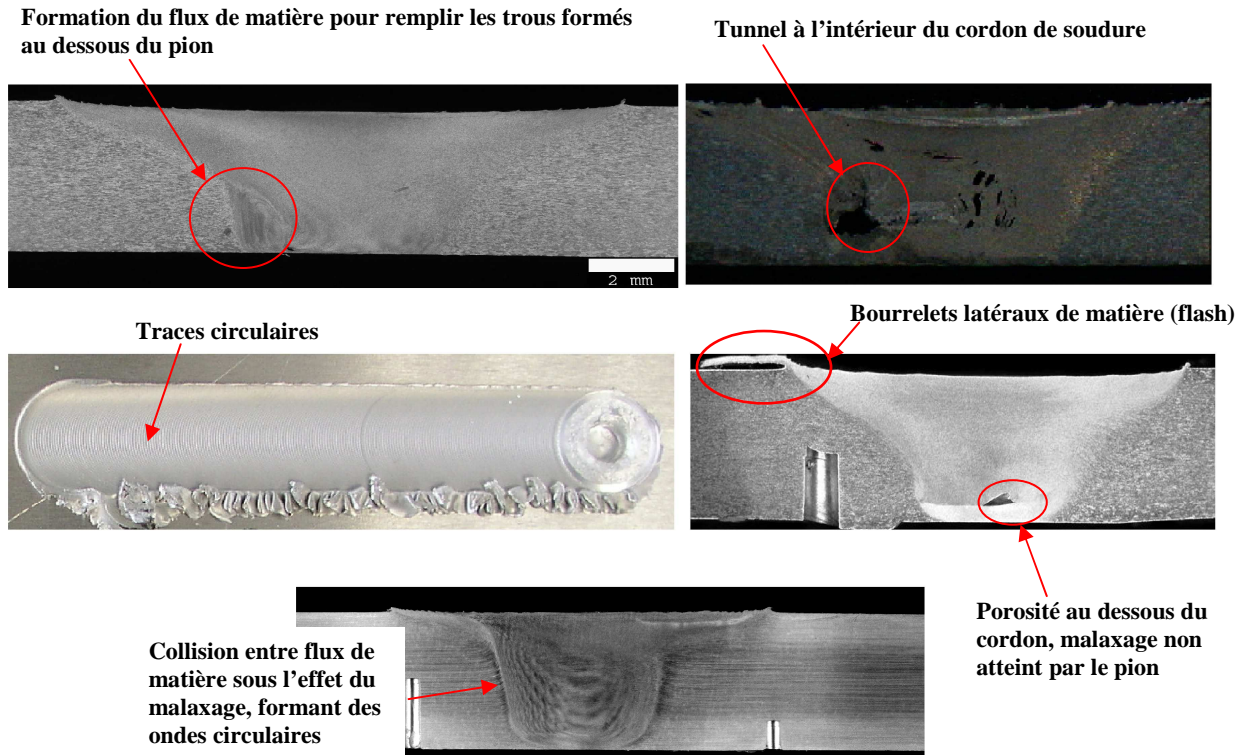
Défauts et Flux de matière observés sur des cordons de soudure de l'aluminium 7020-T6 [IS].
